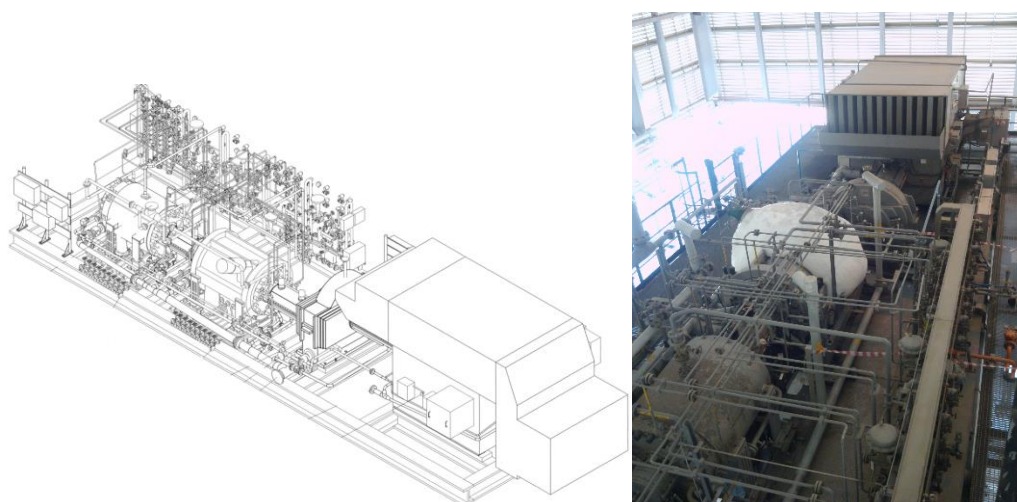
Компрессор отпарного газа с приводным двигателем
